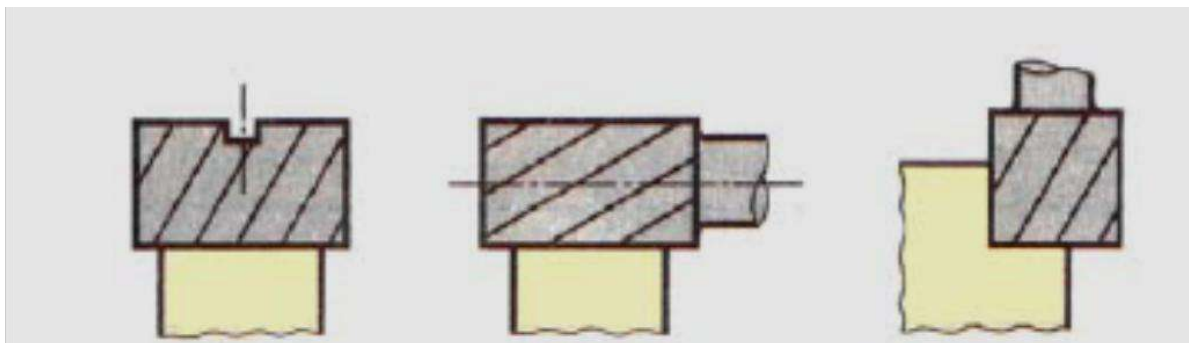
Surfacage en bout, en roulant et fraisage combiné
